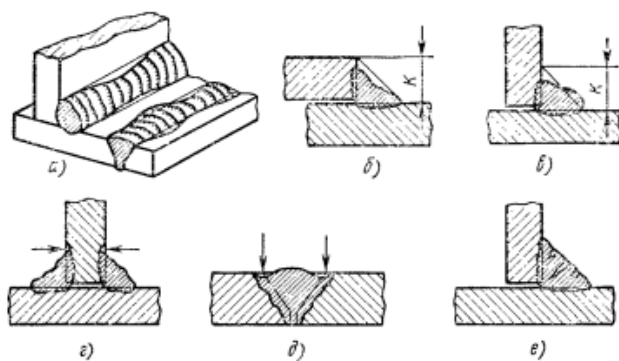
Внешние дефекты сварных соединений:
